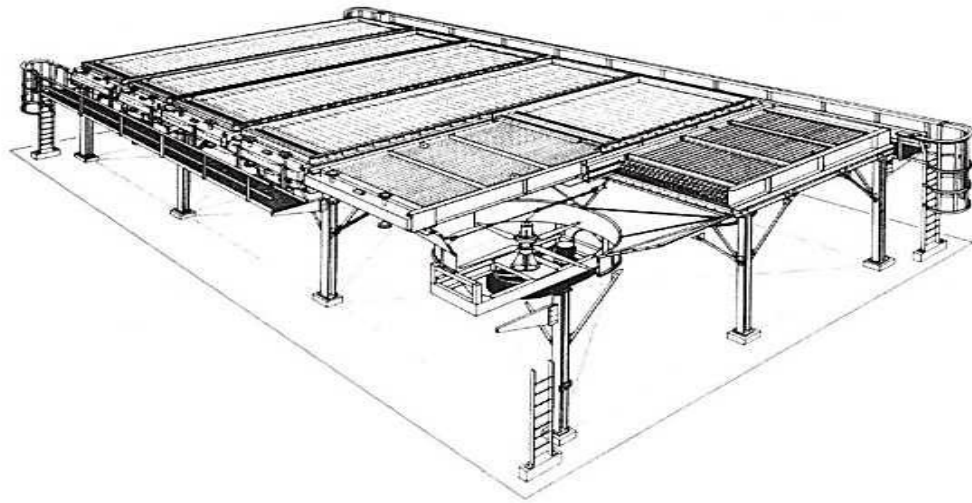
Vue d'ensemble d'un aéro-réfrigérant. [23]
